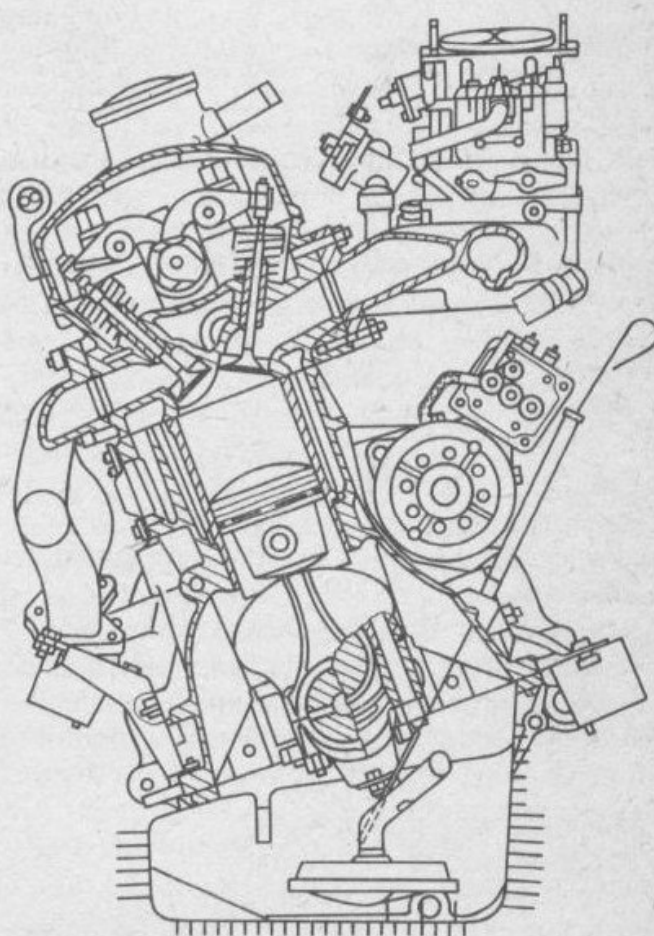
Motor der Moskwitsch-Typen 412/2140 im Schnitt
